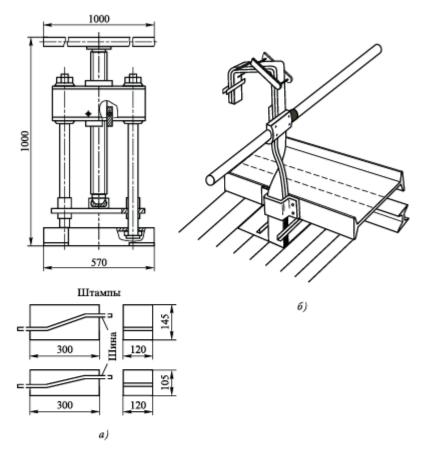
Пресс и штампы для изгибания шин «уткой» (а) и приспособления для изгибания шин «штопором» (б)
